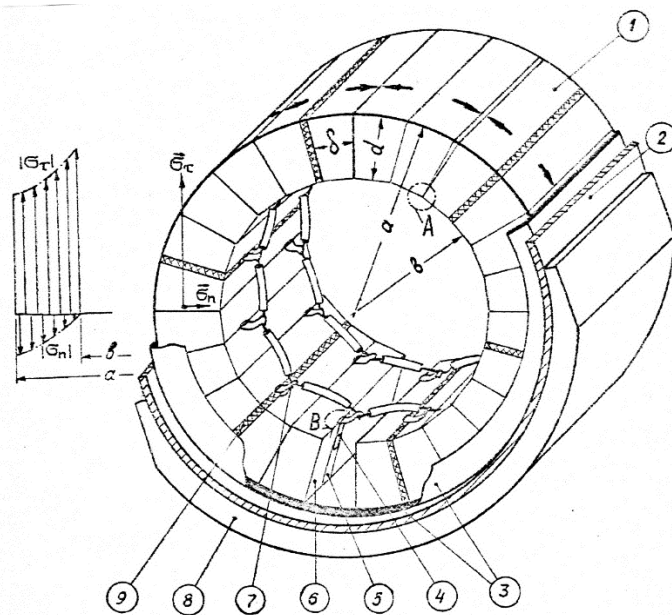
Циліндричний прилад силової конструкції. 1 – активний елемент; 2 – стальний бандаж; 3 – електроізоляційний шар; 4 – монтажний пелюсток; 5 – канавка; 6 – грань призми; 7 – підвісний проводний монтаж; 8 – акустичний екран; σ_τ і σ_n – тангенціальні і нормальні напруження в активному елементі; стрілки показують напрям поляризації призм.
